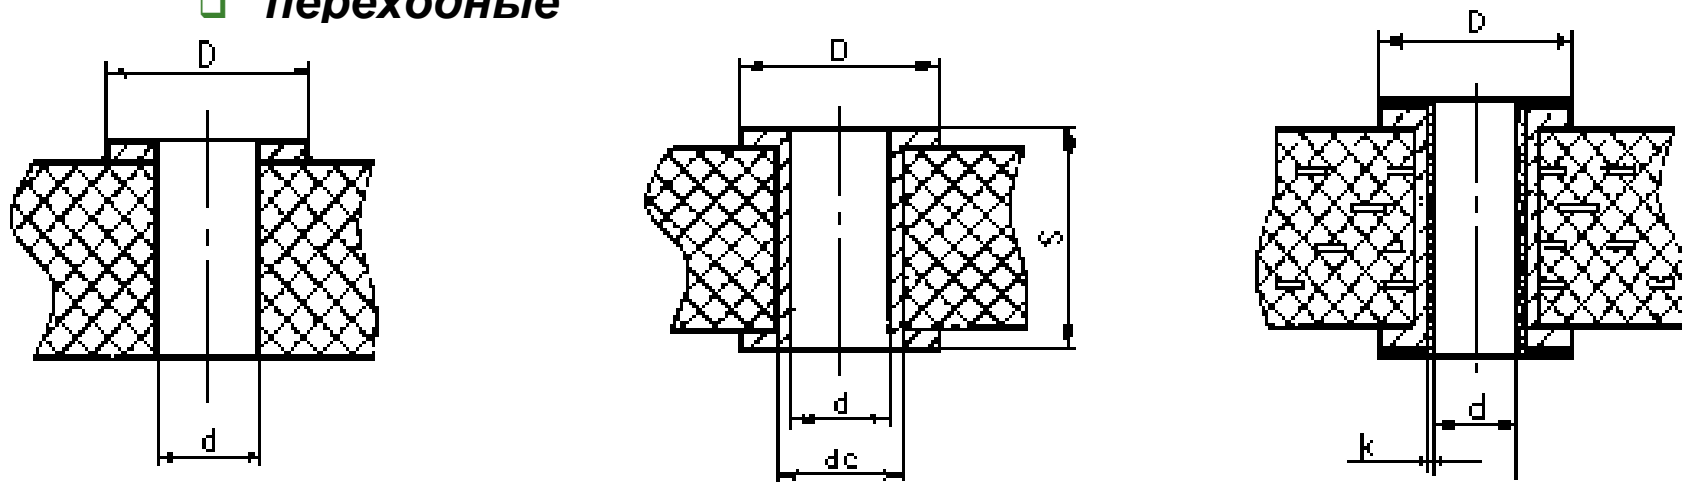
Основные варианты конструкций отверстий печатных плат:
